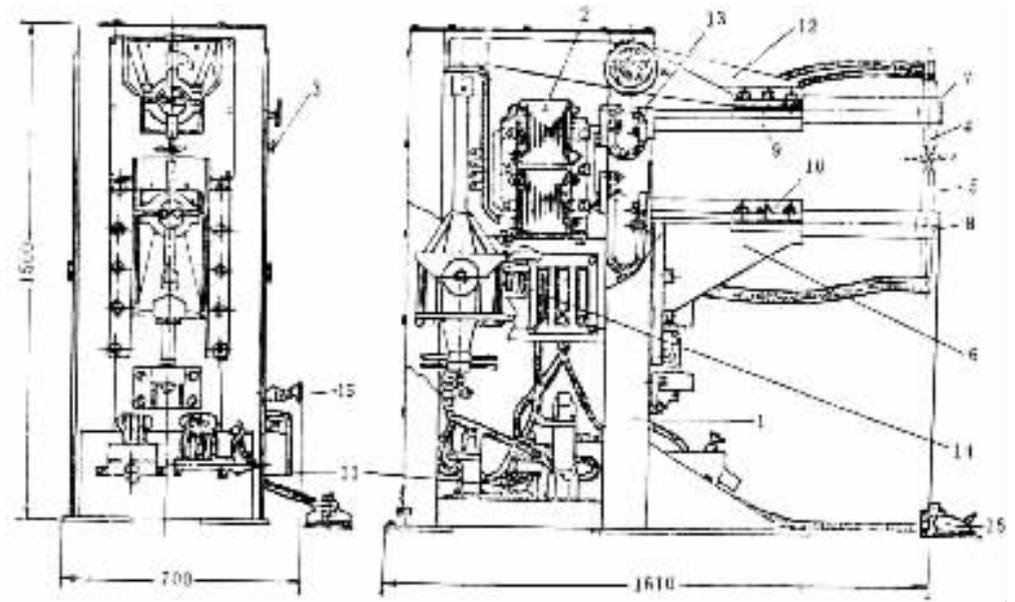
DN3-75/100 型点焊机结构示意图
